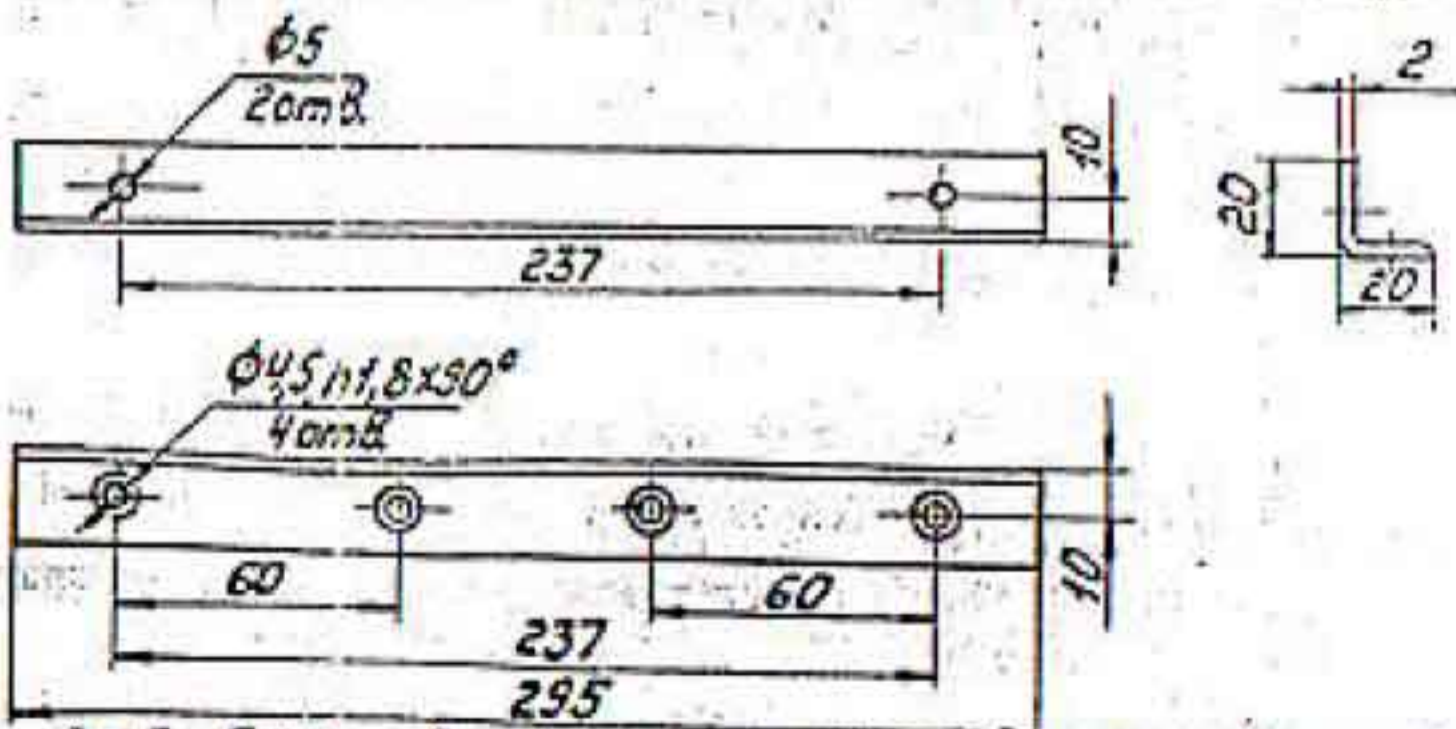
Детали: Ветали для крепления щитов в виде стойки (2шт) и щитового крепления
